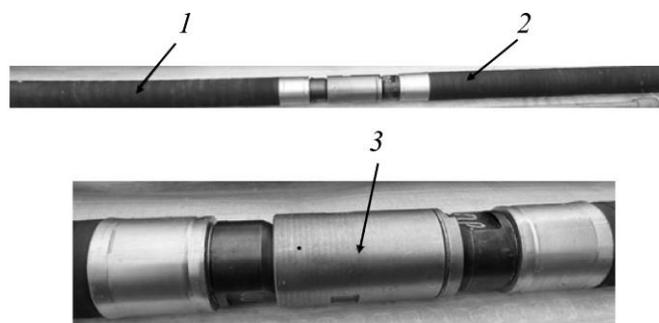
Разрывное устройство: 1, 2 — упруго расширяющийся рукав; 3 — клапан разрыва
